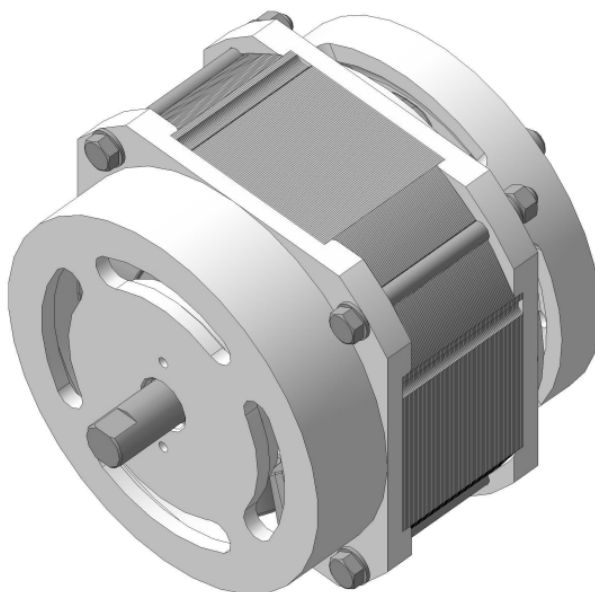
Внешний вид двигателя для привода маслобойки
